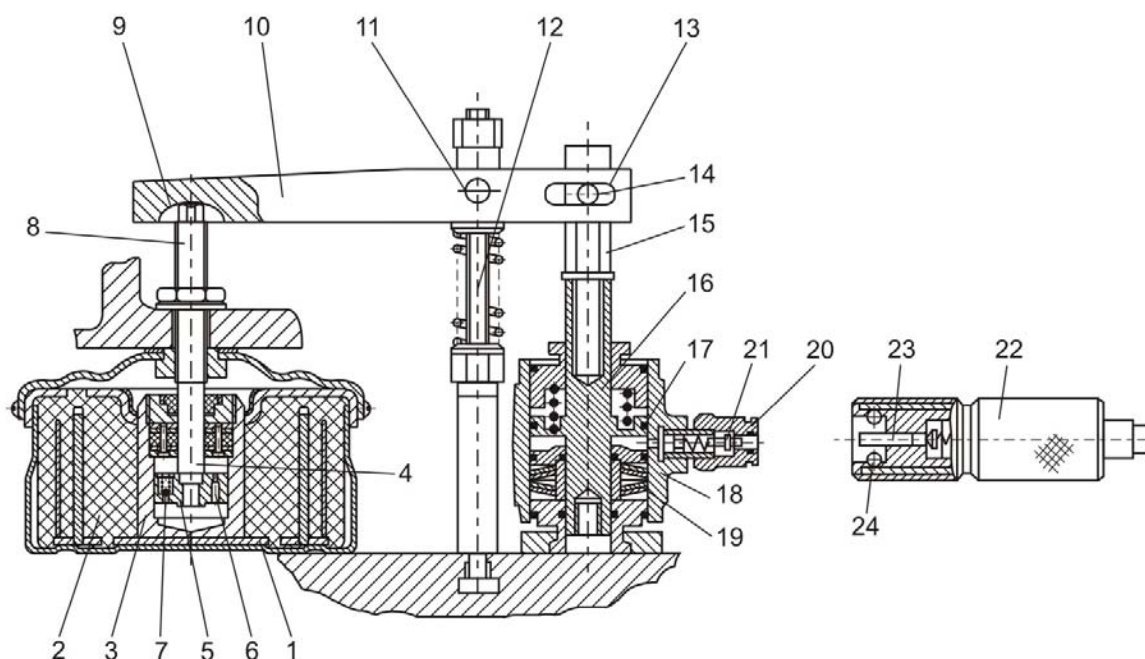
Общий вид виброизолирующего устройства: 1 – основание; 2 – резиновый элемент; 3 – цилиндр; 4 – шток; 5 – поршень; 6 – калиброванное отверстие; 7 – клапан сжатия; 8 – регулировочный винта; 9 – сферическая поверхность лунки; 10 – прихвата; 11 – ось; 12 – стойка; 13 – продольный паз; 14 – ось; 15 – опора; 16 – опорный шток; 17 – поршень; 18 – гидроцилиндр; 19 – пружинный аккумулятор; 20 – малая полумуфта; 21 – клапан; 22 – большая полумуфта; 23 – клапанный штырь; 24 – шарики
